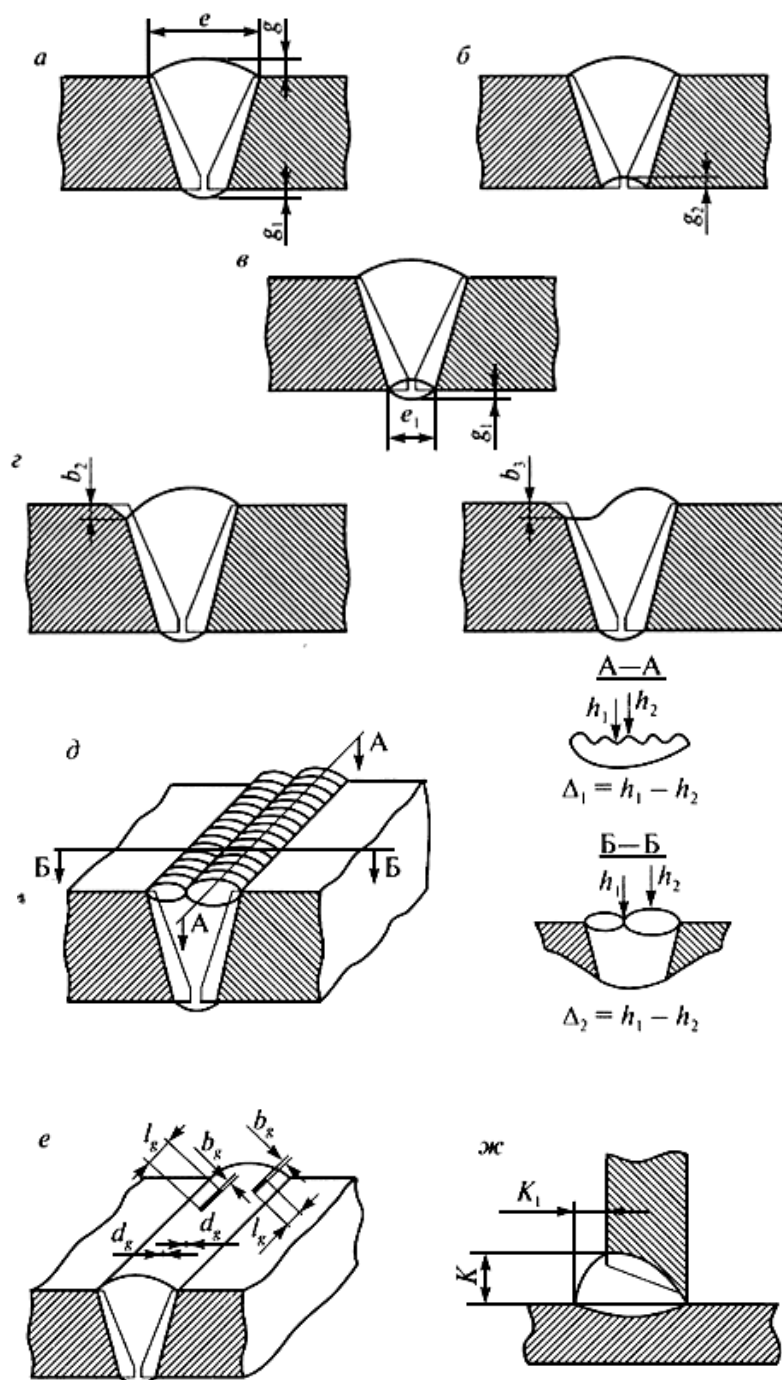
Конструктивные элементы и дефекты сварного шва, подлежащие измерительному контролю (начало): а, б – размеры (ширина, высота) стыкового одностороннего шва с наружной и внутренней стороны; в – то же двухстороннего сварного шва; г – подрез и неполное заполнение разделки кромок; д – чешуйчатость (Δ_1) шва и западание между валиками шва (Δ_2); е – размеры поверхностных включений (диаметр – d_g ; длина – l_g ; ширина – b_g включения); ж – размеры катета шва углового (таврового, нахлесточного) соединения
